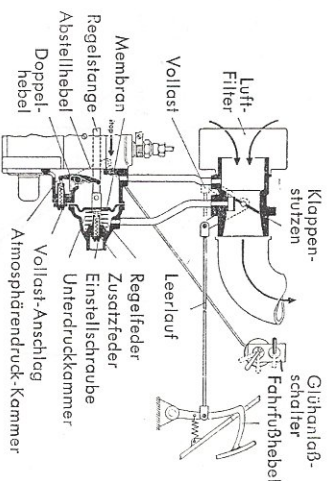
Schema eines pneumatischen Reglers; Membranblock mit Zusatzfeder (straubdichte Ausführung)
